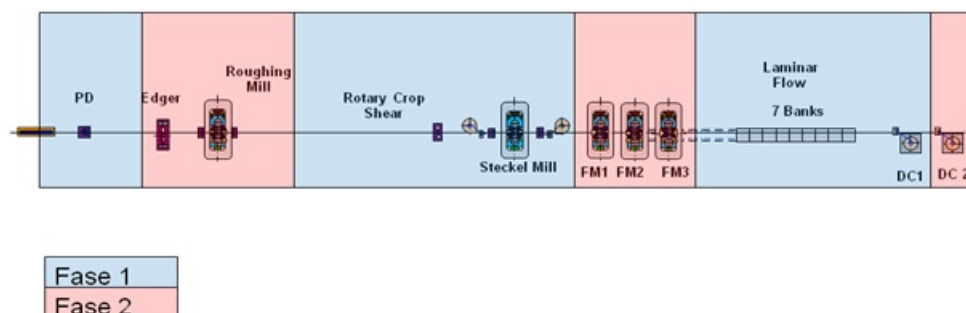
Layout do novo laminador de tiras a quente da Gerdau Ouro Branco.
